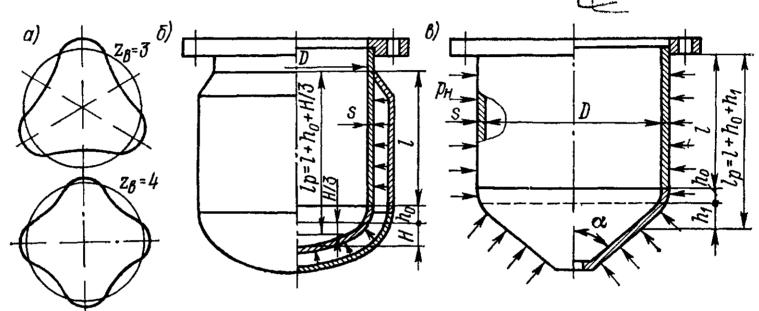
Схемы к определению расчетной длины цилиндрической обечайки: a — волны смятия; δ — корпус аппарата с эллиптическим днищем и рубашкой; ϵ — корпус аппарата с коническим днищем
